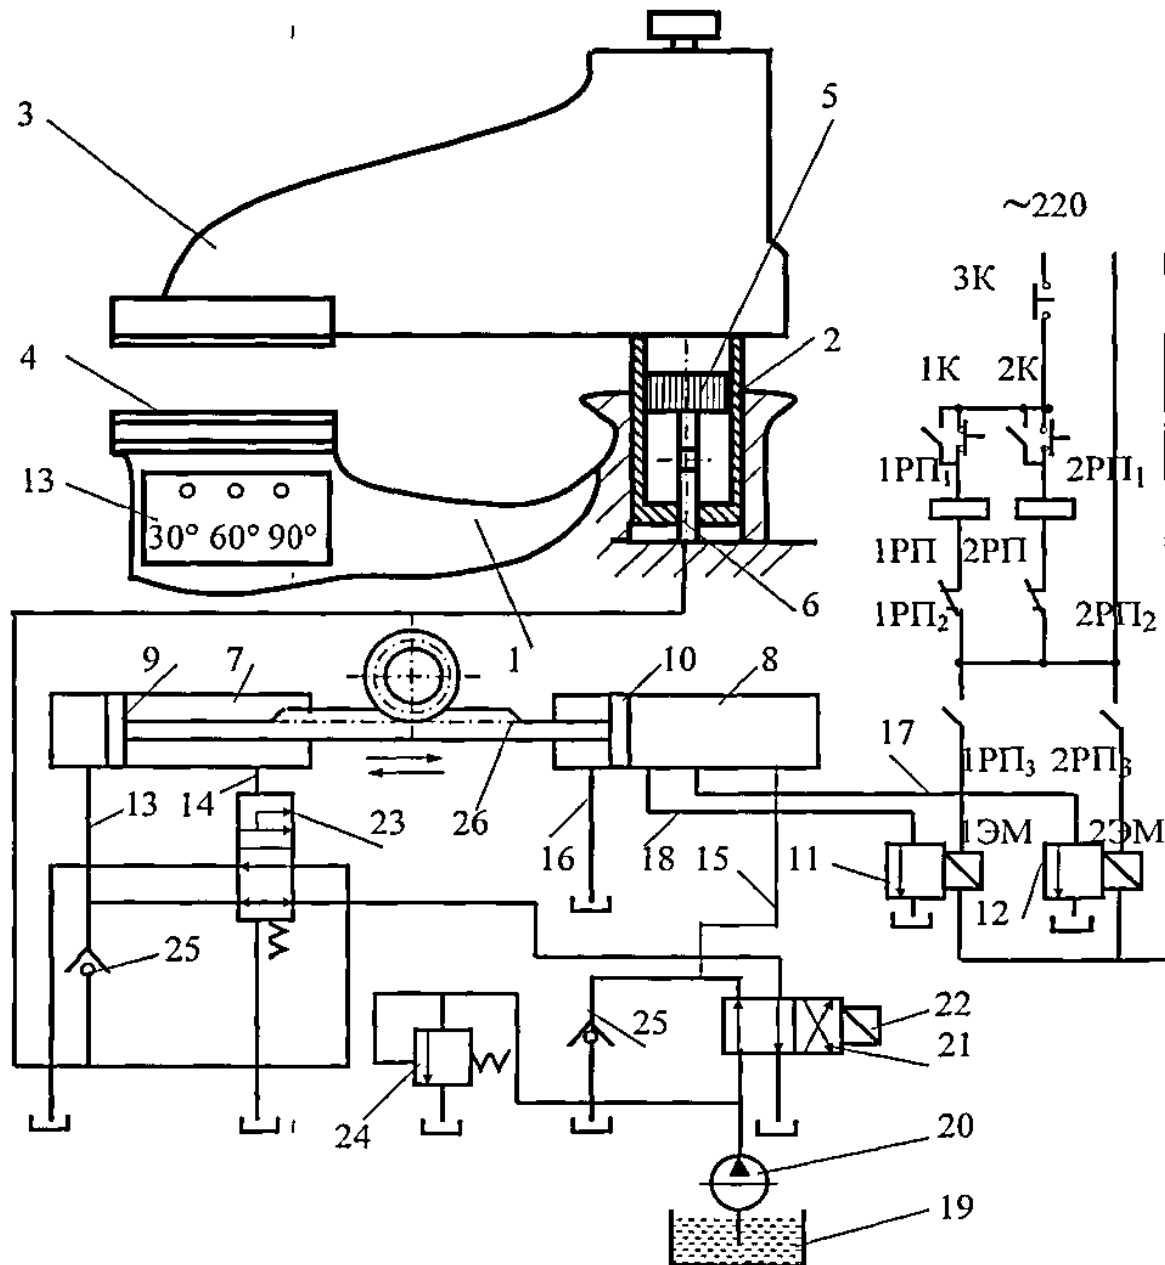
Вырубочный консольный пресс с регулируемым поворотом ударника
